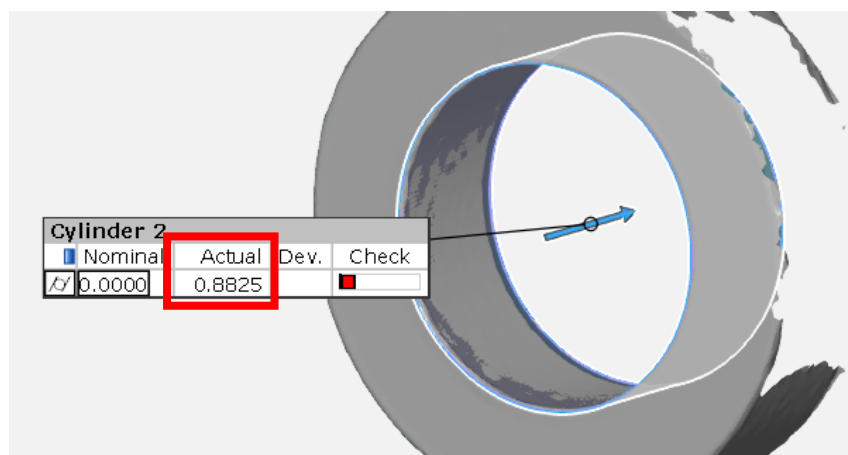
Escaneo 3, posición 1 (3.1.). Tolerancia de cilindridad. Anillo patrón. Escáner EinScan
